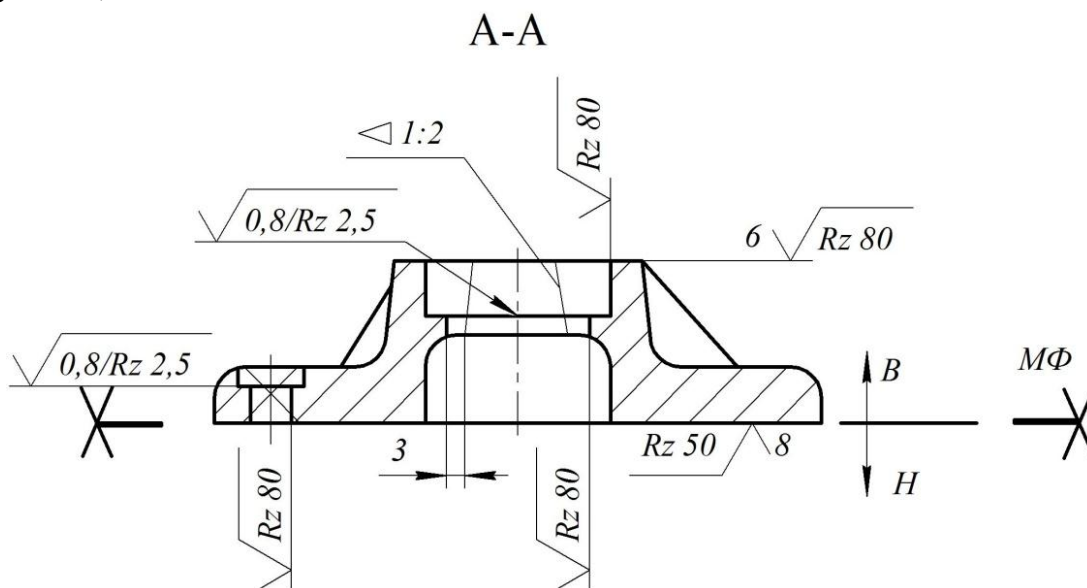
Правила обозначения припусков на отливках простой формы
